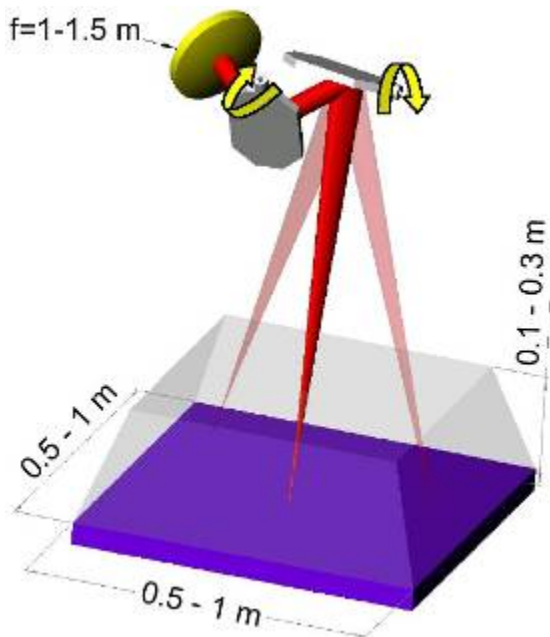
Prinzip des Scanner- Schweißens
